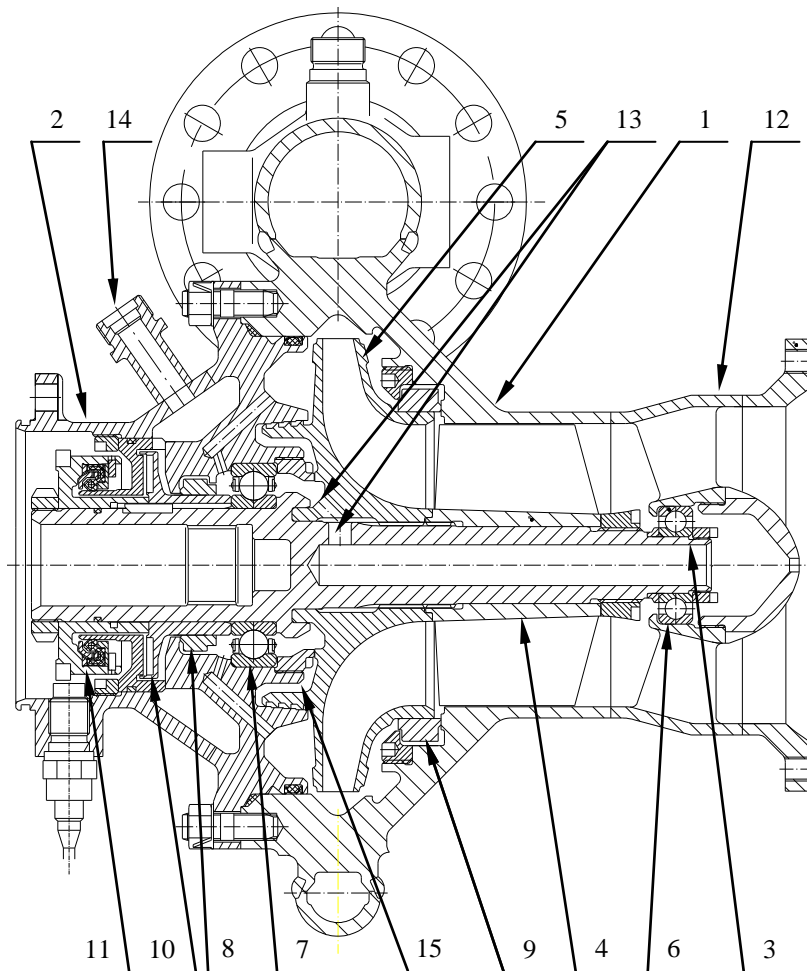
Насос керосина: 1 – корпус; 2 – крышка; 3 – вал; 4 – шнек; 5 – крыльчатка; 6 и 7 – подшипники; 8 и 9 – плавающие кольца; 10 – импеллер; 11 – стояночное уплотнение; 12 – входной патрубок; 13 – перепускные отверстия; 14 – штуцер сброса утечки; 15 – полость автоматического разгрузочного устройства
